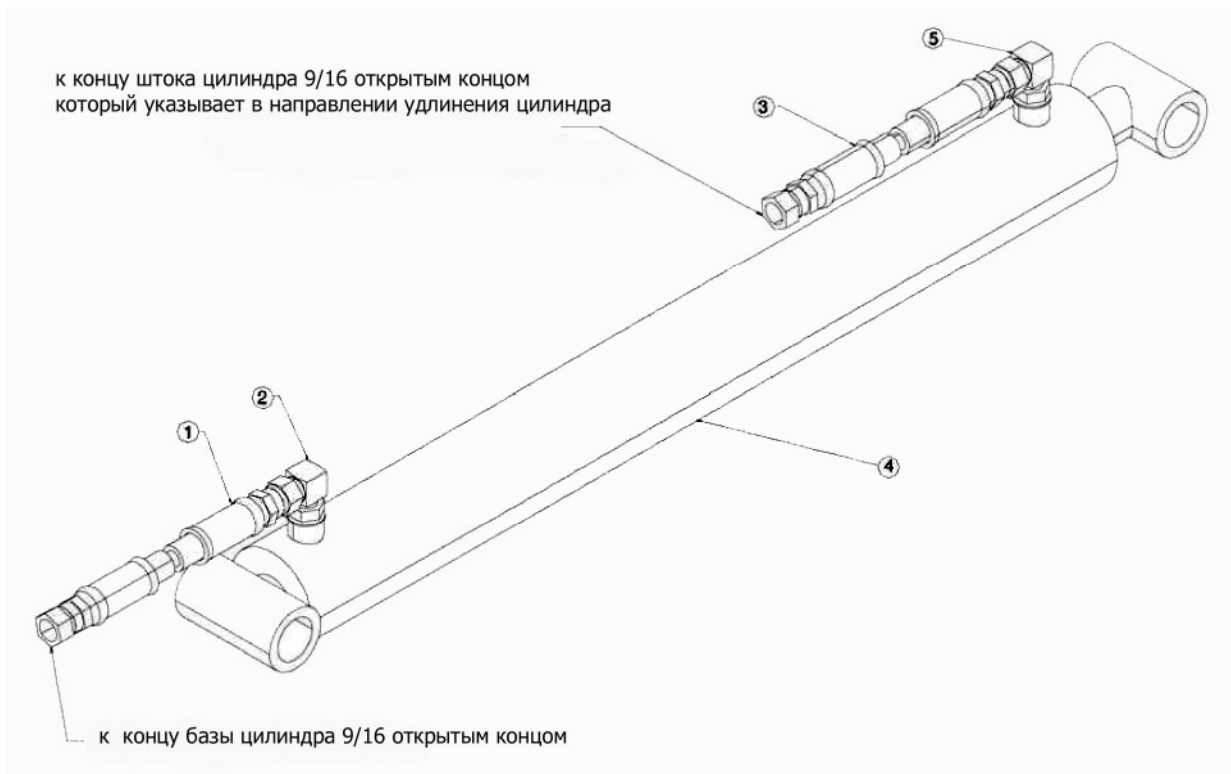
Чертеж RPU зажимающего цилиндра - A2300-35
